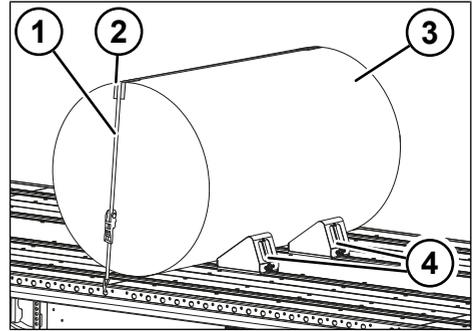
Bloccaggio trasversale della bobina di carta
